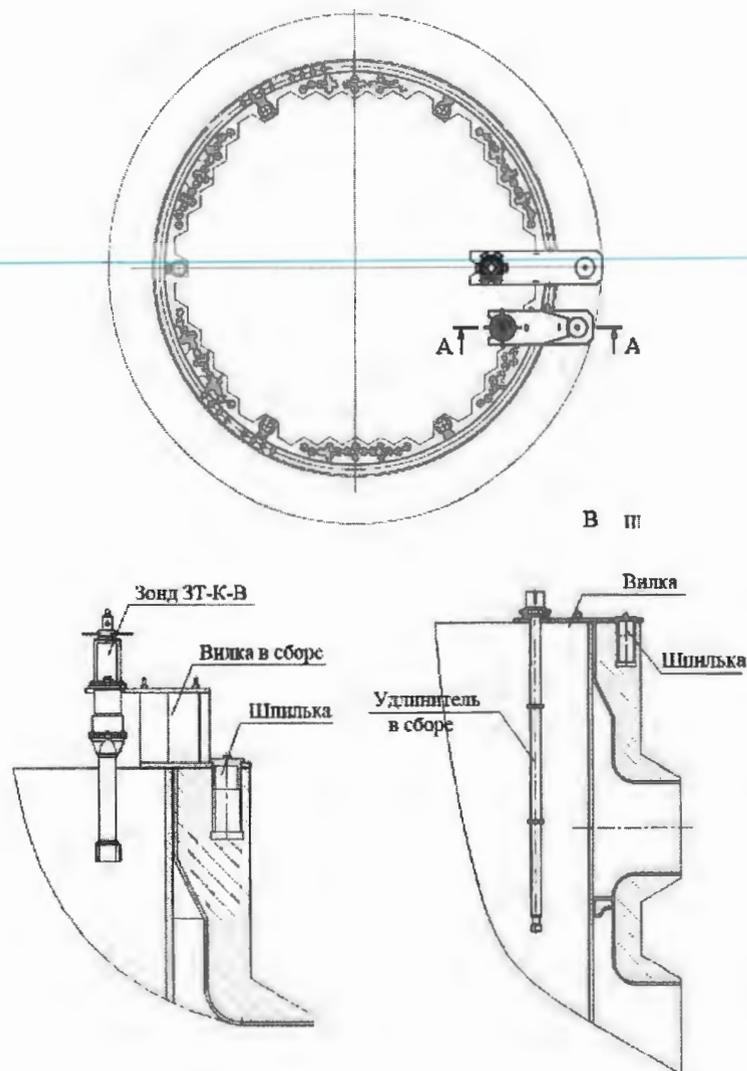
Схема расположения зонда ЗТ-К-В и удлинителя в сборе на плоскости главного разреза корпуса реактора
